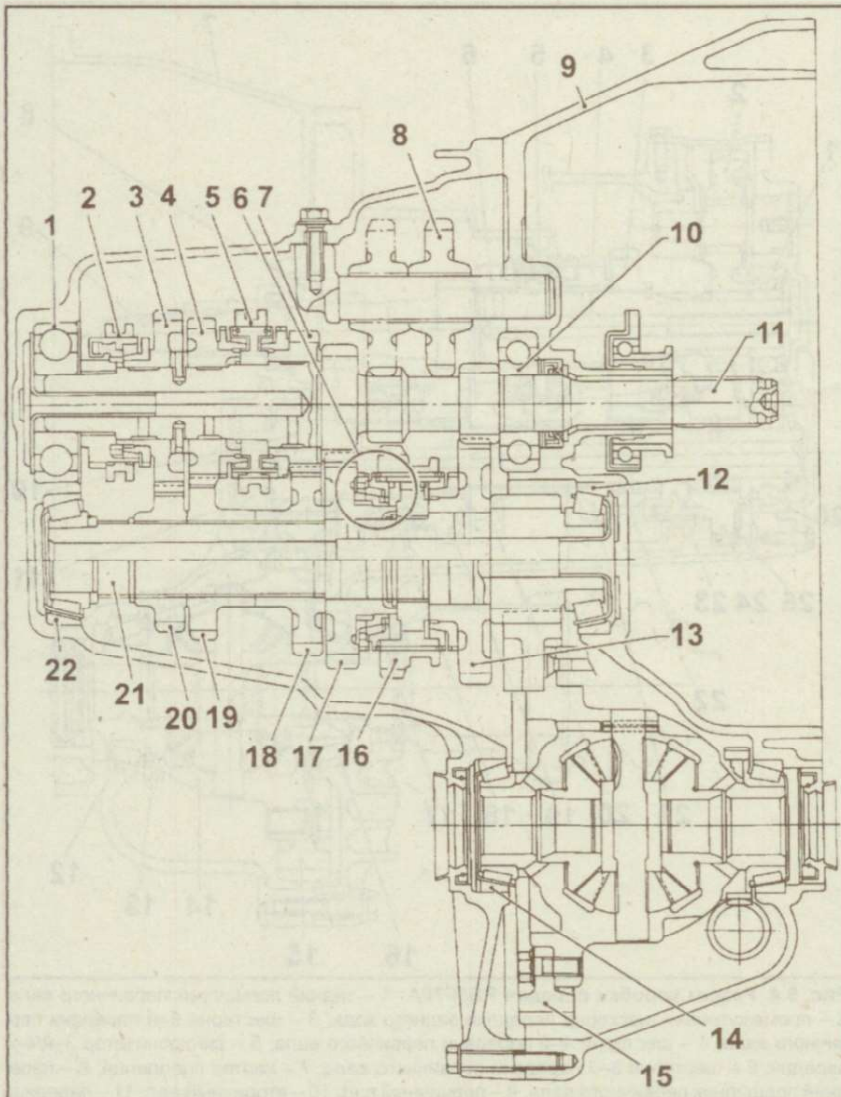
Разрез коробки передач RS5F50A: 1 – задний подшипник первичного вала; 2 – синхронизатор 5-й передачи; 3 – шестерня 5-й передачи первичного вала; 4 – шестерня 4-й передачи первичного вала; 5 – синхронизатор 3-й/4-й передач; 6 – синхронизатор 1-й/2-й передач с двойным блокирующим кольцом; 7 – шестерня 3-й передачи первичного вала; 8 – промежуточная шестерня передачи заднего хода; 9 – картер сцепления; 10 – передний подшипник первичного вала; 11 – первичный вал; 12 – передний подшипник вторичного вала; 13 – шестерня 1-й передачи вторичного вала; 14 – подшипник дифференциала; 15 – главная передача; 16 – шестерня передачи заднего хода вторичного вала; 17 – шестерня 2-й передачи вторичного вала; 18 – шестерня 3-й передачи вторичного вала; 19 – шестерня 4-й передачи вторичного вала; 20 – шестерня 5-й передачи вторичного вала; 21 – вторичный вал; 22 – задний подшипник вторичного вала
